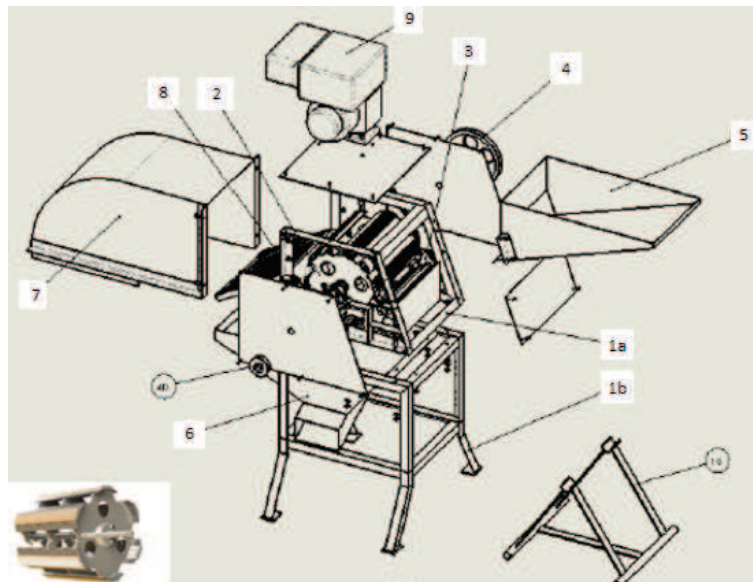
Vista explosionada de máquina trilladora con cilindro de barras
